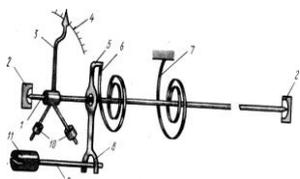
Установка подвижной части измерительного механизма на опорах
